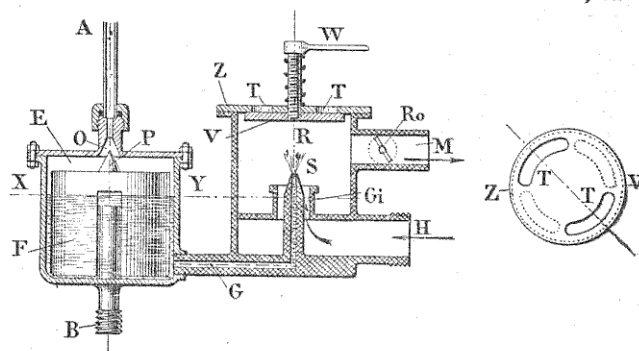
Carburateur, vue extérieure et coupe (schéma).
